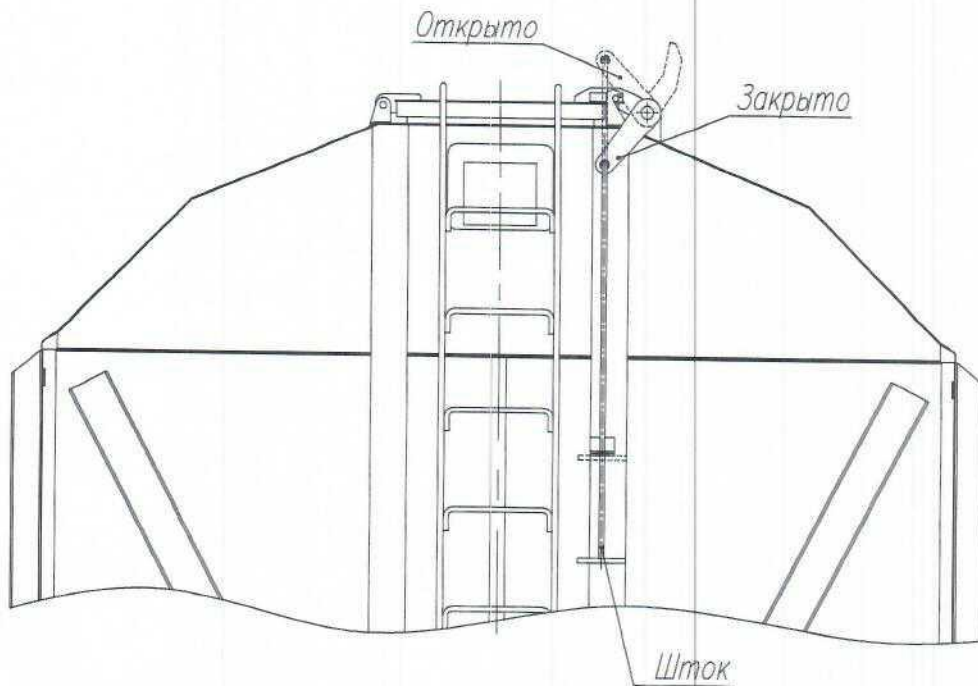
Положения механизма блокировки загрузочных люков
